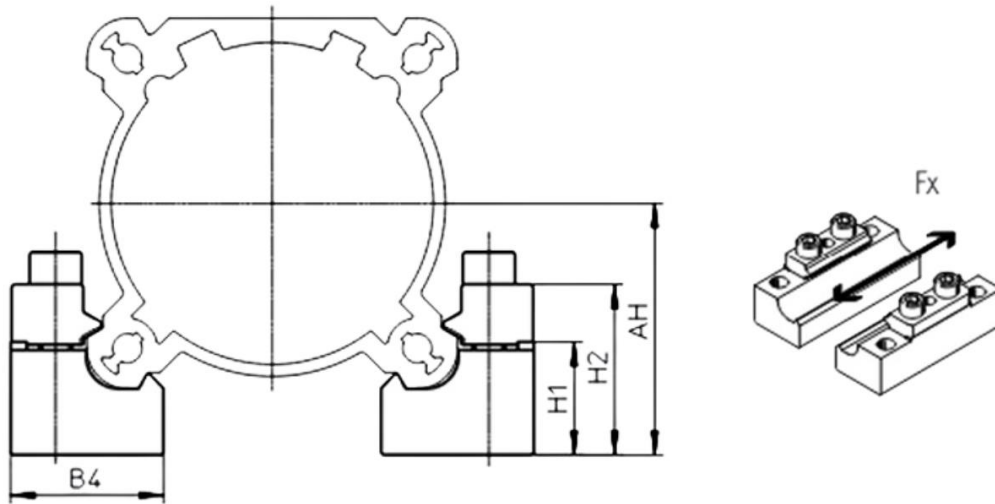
Morsetti per il fissaggio del cilindro elettrico
